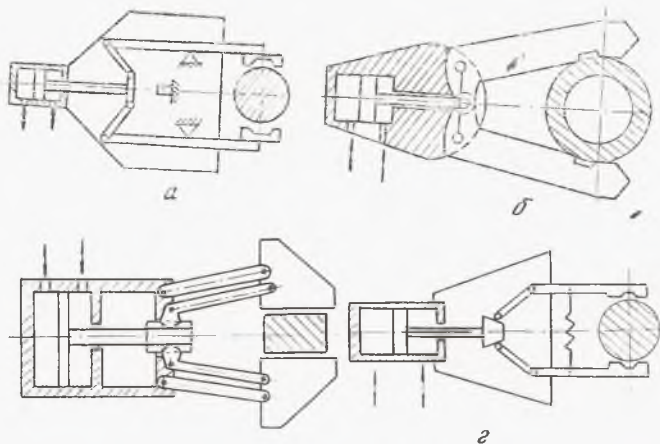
Механические захватные устройства: а — рычажный; б — кулачково-рычажный; в — реечно-рычажный; г — клино-рычажный
